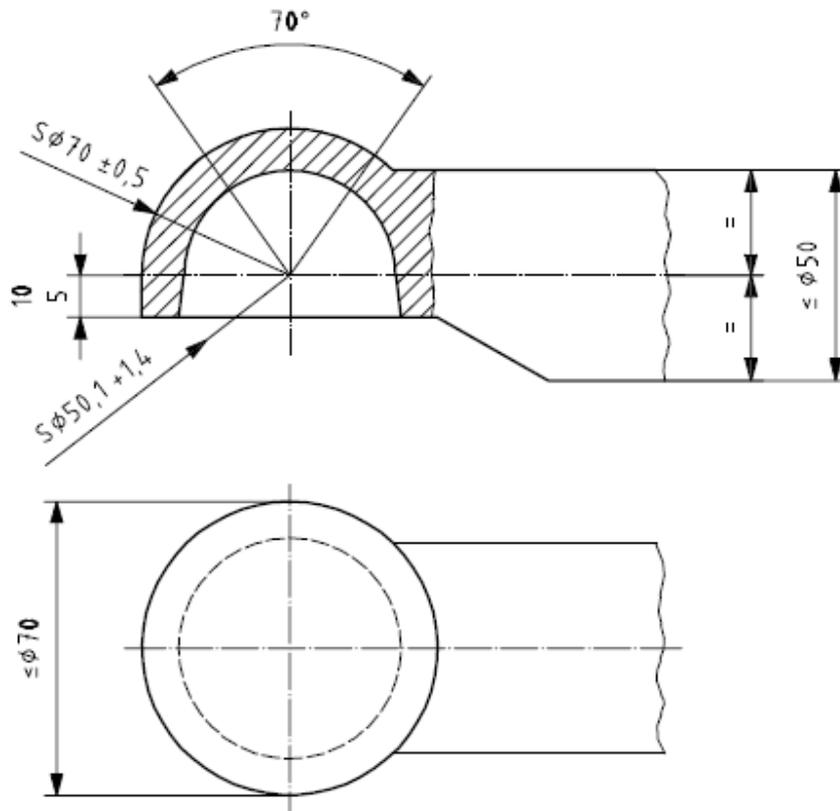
Dimensiones del punto (o los puntos) de conexión del remolque
